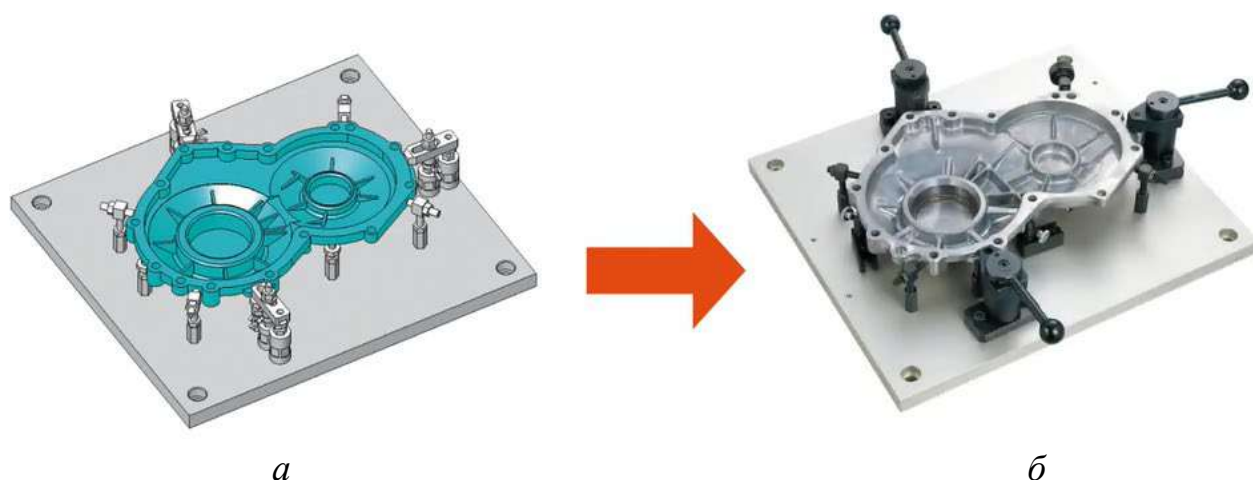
Закріплення заготовки на універсальному пристрої:
